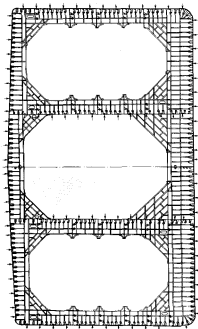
Участок перекрытия сунгарника без второго дна с двумя продольными переборками (три показаны переборками по ширине)
